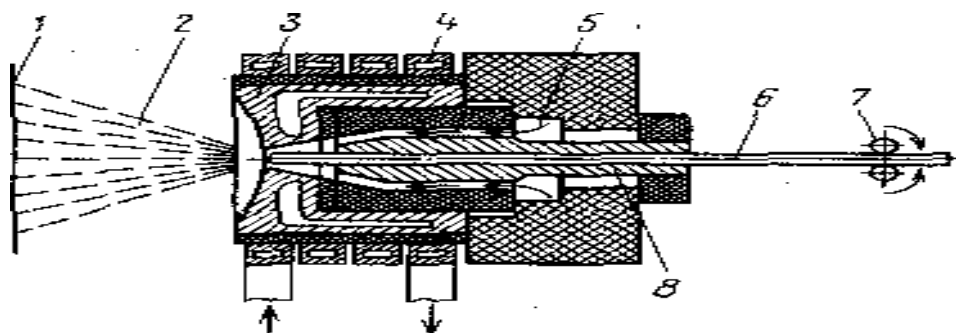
Розпорошувальна голівка високочастотного пристрою для напilenня: 1 - напилювана поверхня; 2 - газометалічний струмінь; 3 - концентратор струму; 4 - індуктор ТВЧ; 5 - повітряний канал; 6-проволока; 7 - подаючі ролики; 8 - втулка напрямної.
